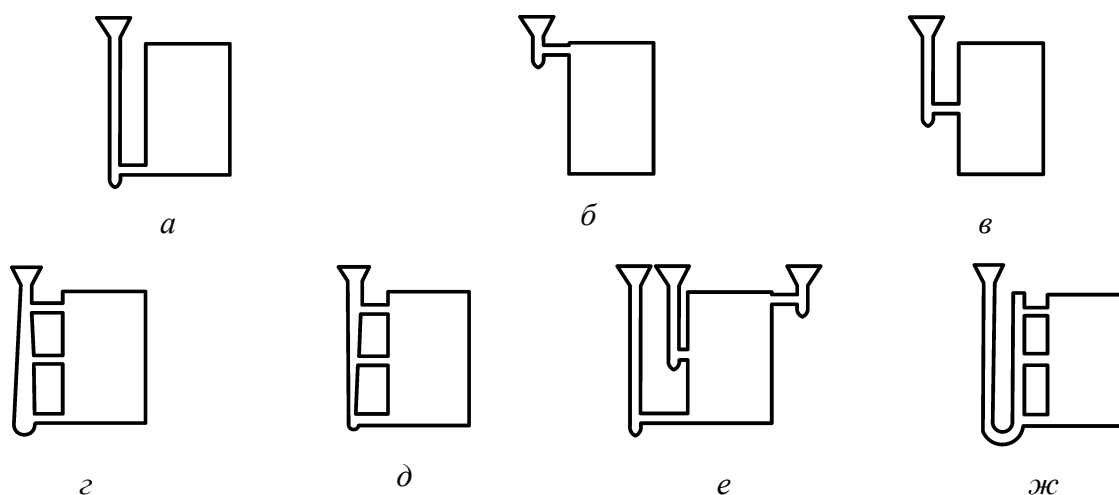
Подвод металла к отливке: *а* – сифонная заливка; *б* – заливка сверху; *в* – заливка в середину отливки; *г* – ступенчатая расширяющаяся литниковая система; *д* – ступенчатая сужающаяся литниковая система; *е* – заливка через несколько самостоятельных литников; *ж* – сифонная ступенчатая литниковая система
